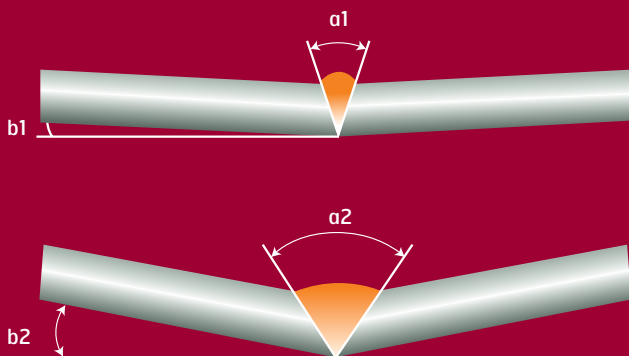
Pré-positionnement d'une soudure d'angle et d'une soudure en V.
